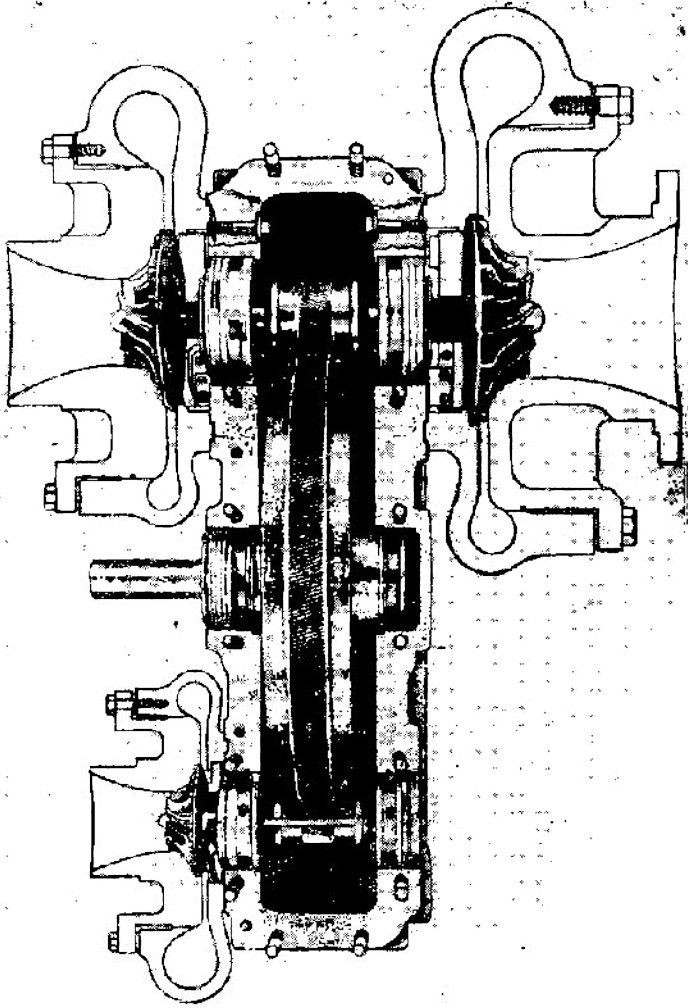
Зовнішній вигляд двовального компресора типу "DEMAG"
